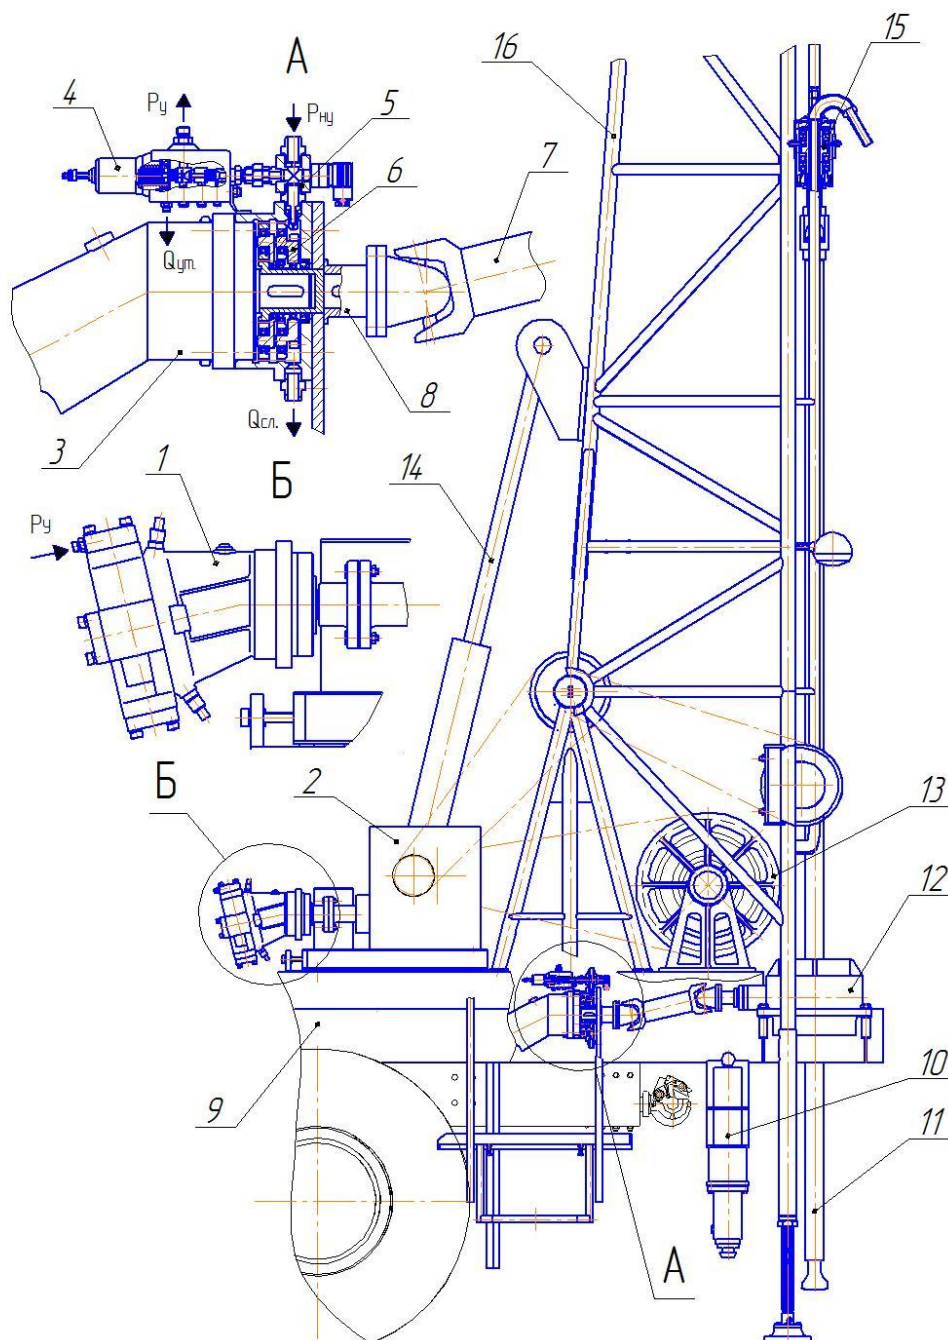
Общий вид МБМ: 1 — гидромотор регулируемый; 2 — привод подачи инструмента; 3 — гидромотор нерегулируемый; 4 — клапан ГУК; 5 — датчик ГМД; 6 — редуктор; 7 — вал карданный; 8 — муфта; 9 — автошасси; 10 — система аутригеров; 11 — инструмент; 12 — привод главного движения; 13 — лебедка двухбарабанная; 14 — гидроцилиндр подъема (опускания) мачты; 15 — вертлюг; 16 — мачта
